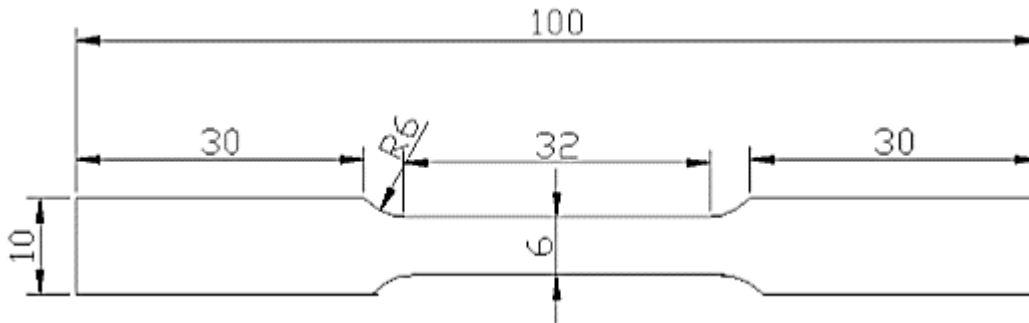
Dimensiones de probetas para ensayo de tracción. (Unidades en mm)
